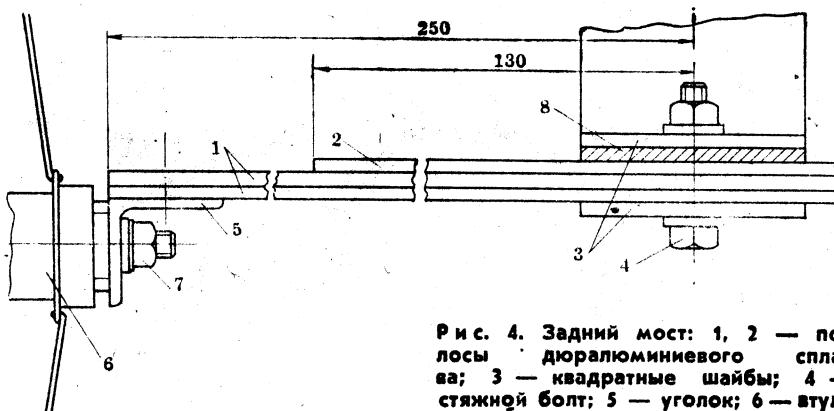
Задний мост: 1, 2 — полосы дюралюминиевого сплава; 3 — квадратные шайбы; 4 — стяжной болт; 5 — уголок; 6 — втулка заднего колеса; 7 — гайка; 8 — нижний пояс рамы.
